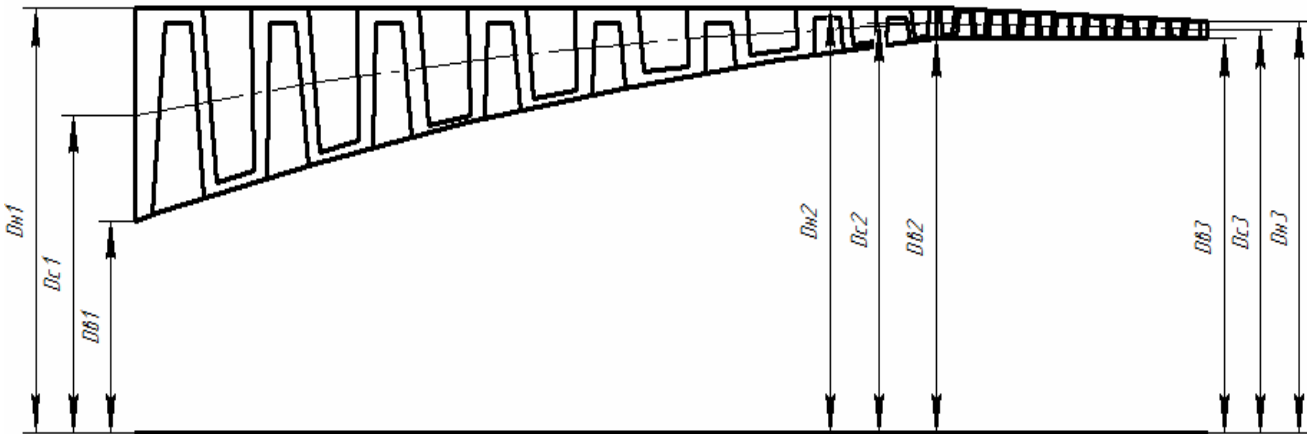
Меридіанний переріз проточної частини компресора ГТД
